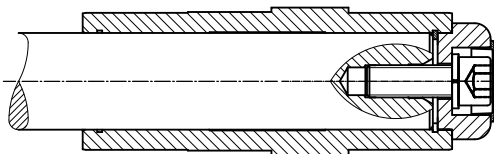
Getriebe auf Welle ohne Anlageschulter mit Befestigungselement befestigt
